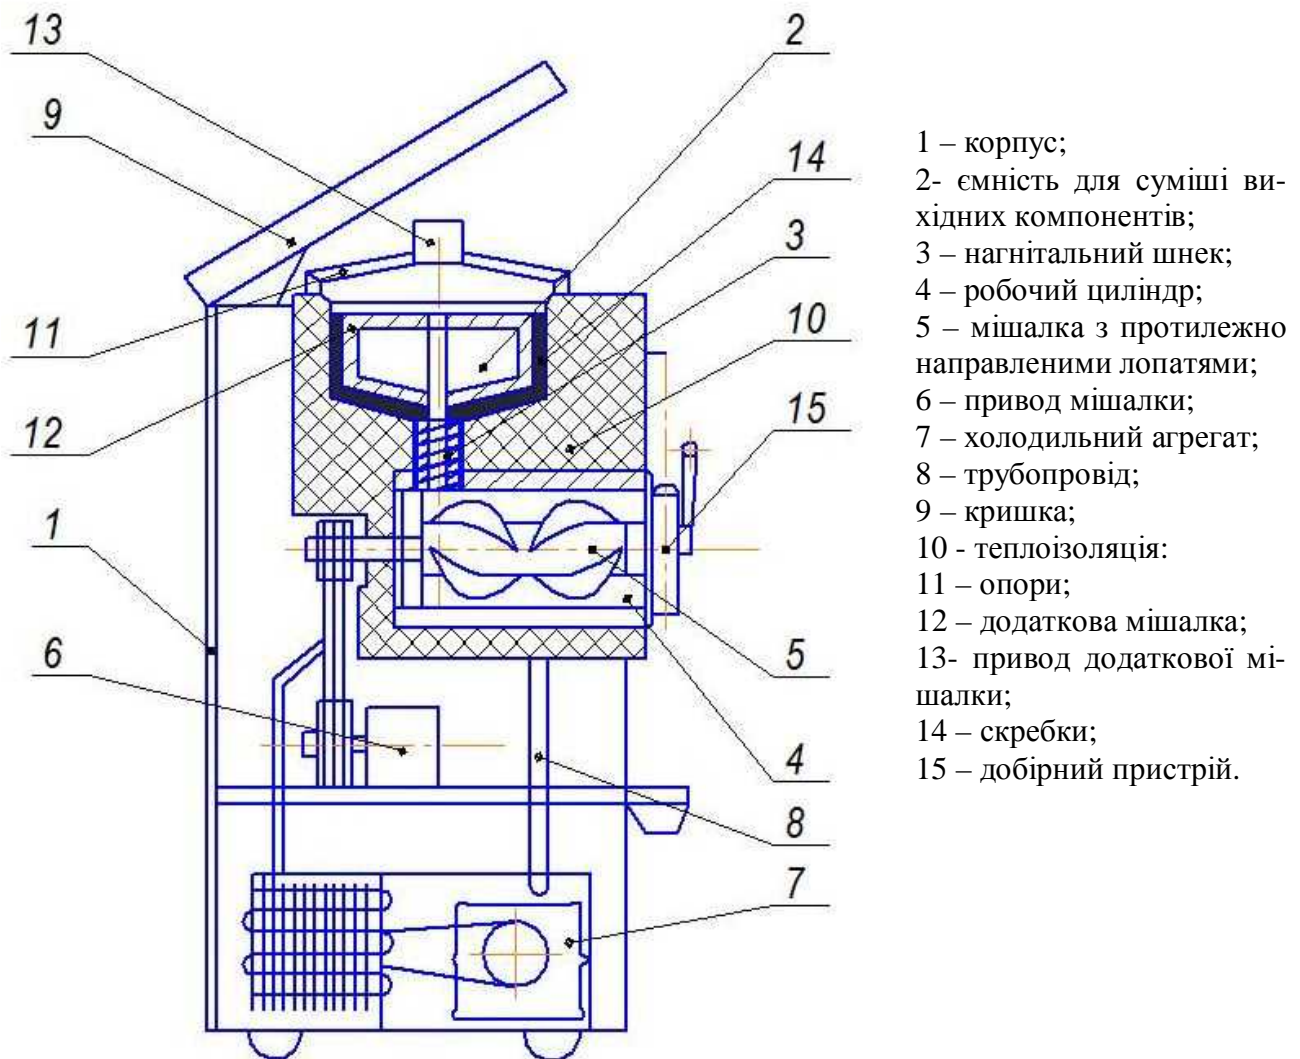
Загальний вид фризера для виготовлення м'якого морозива
